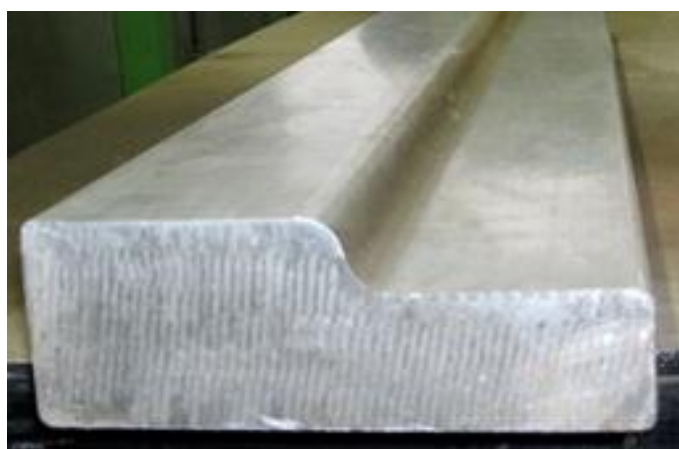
Внешний вид прессованного профиля из сплава В-1469
